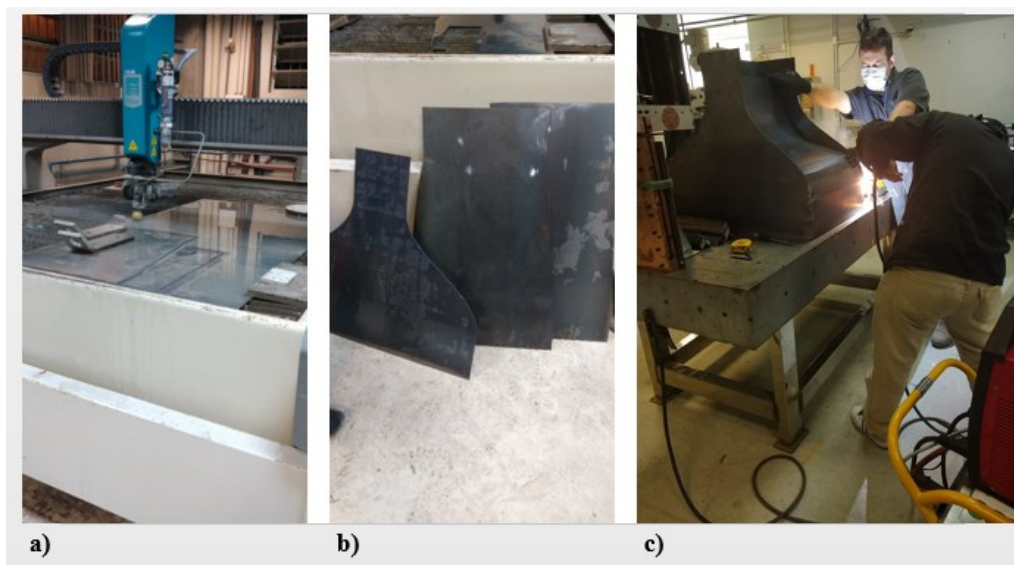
Fabricação do bocal. a) Corte das chapas na máquina de jato de água. b) chapas cortadas. c) placas calandradas sendo soldadas.
